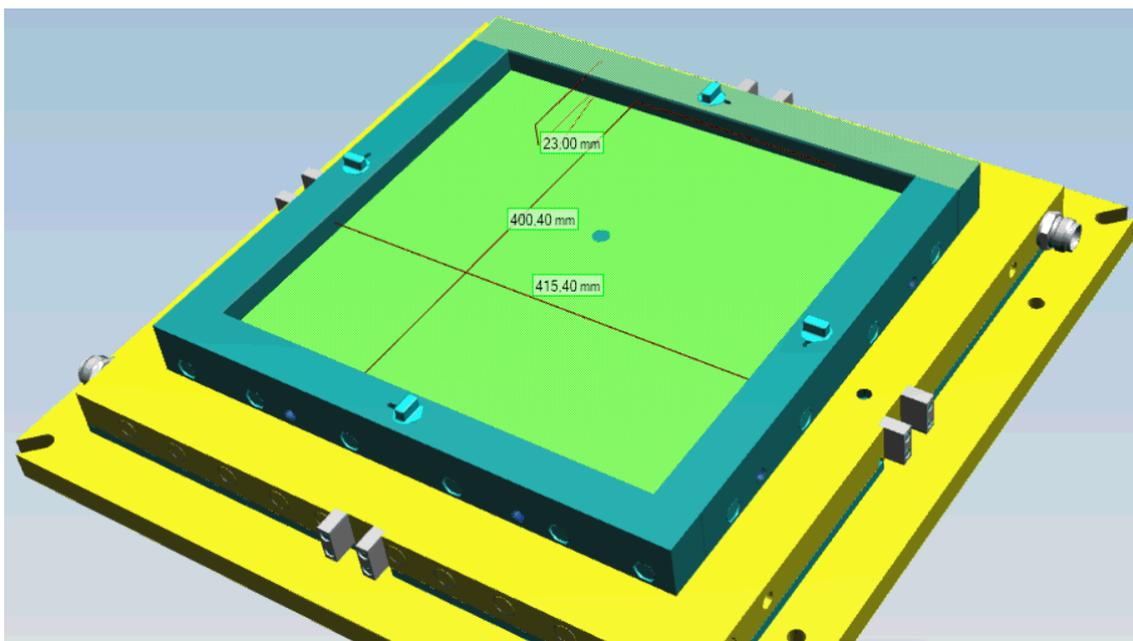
Stammwerkzeug „400 mm x 515 mm“
